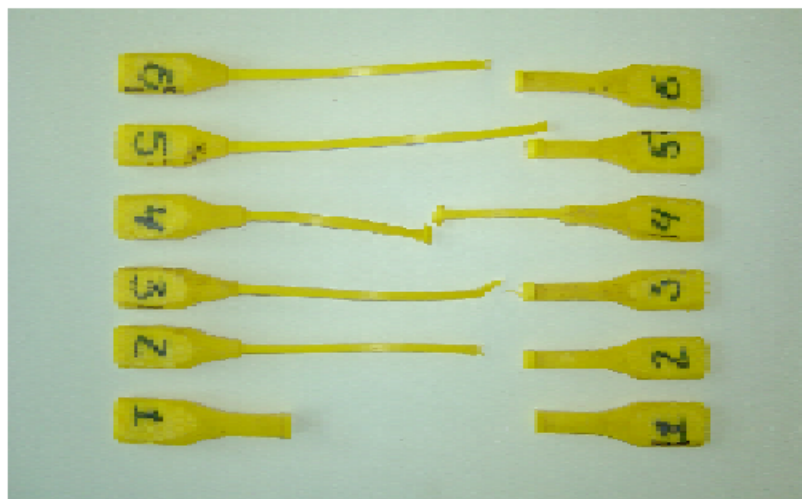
Разрушенные образцы-лопатки со сварным швом.
